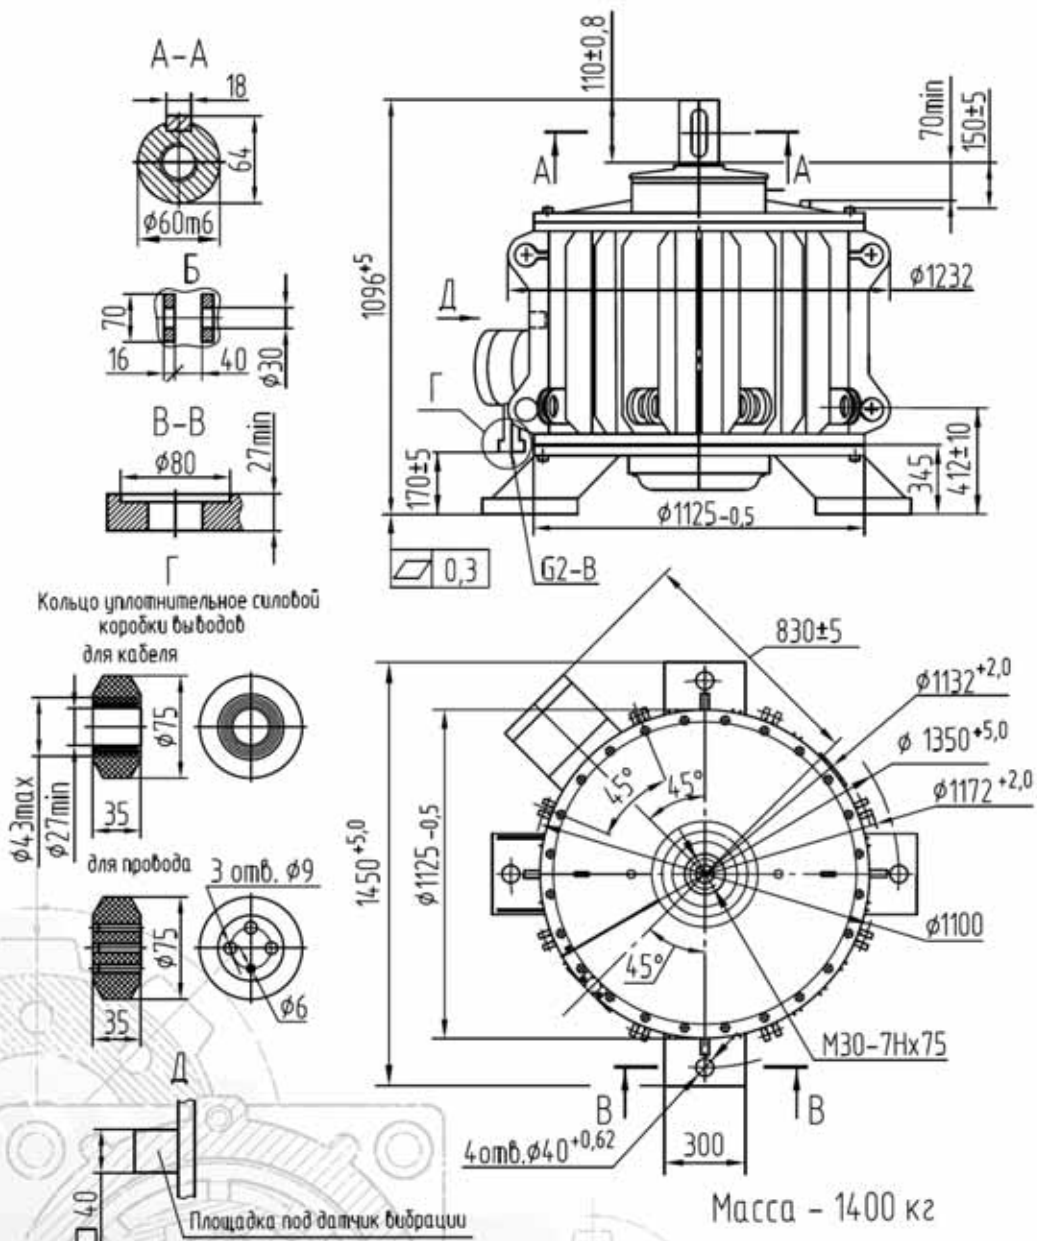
Габаритные, присоединительные размеры и масса двигателя ВАСО5К-37-24 с цилиндрическим концом вала
